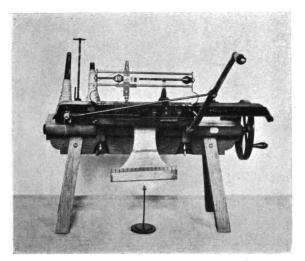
Machine à tricoter (V. Nº 7793.)
